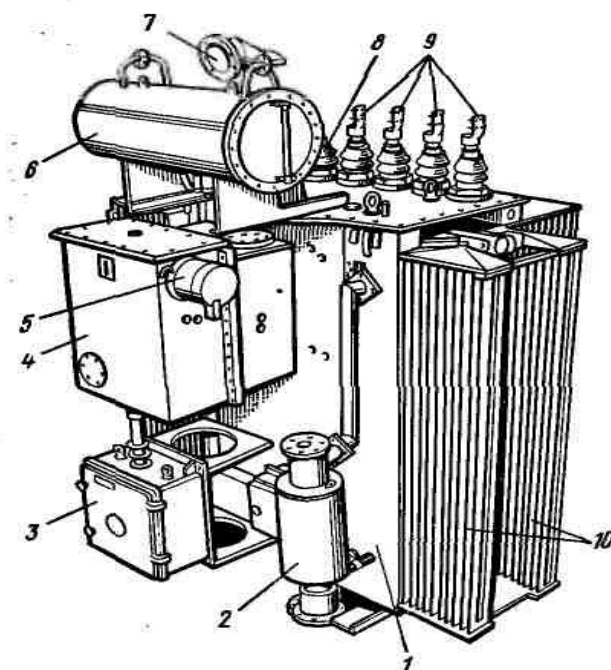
Трансформатор с регулированием напряжения под нагрузкой: 1 — бак; 2 — термосифонный фильтр; 3 — приводной механизм; 4 — бак с контакторами; 5 — муфта; 6 — расширитель; 7 — выхлопная труба; 8 — вводы НН; 9 — вводы ВН; 10 — радиаторы
